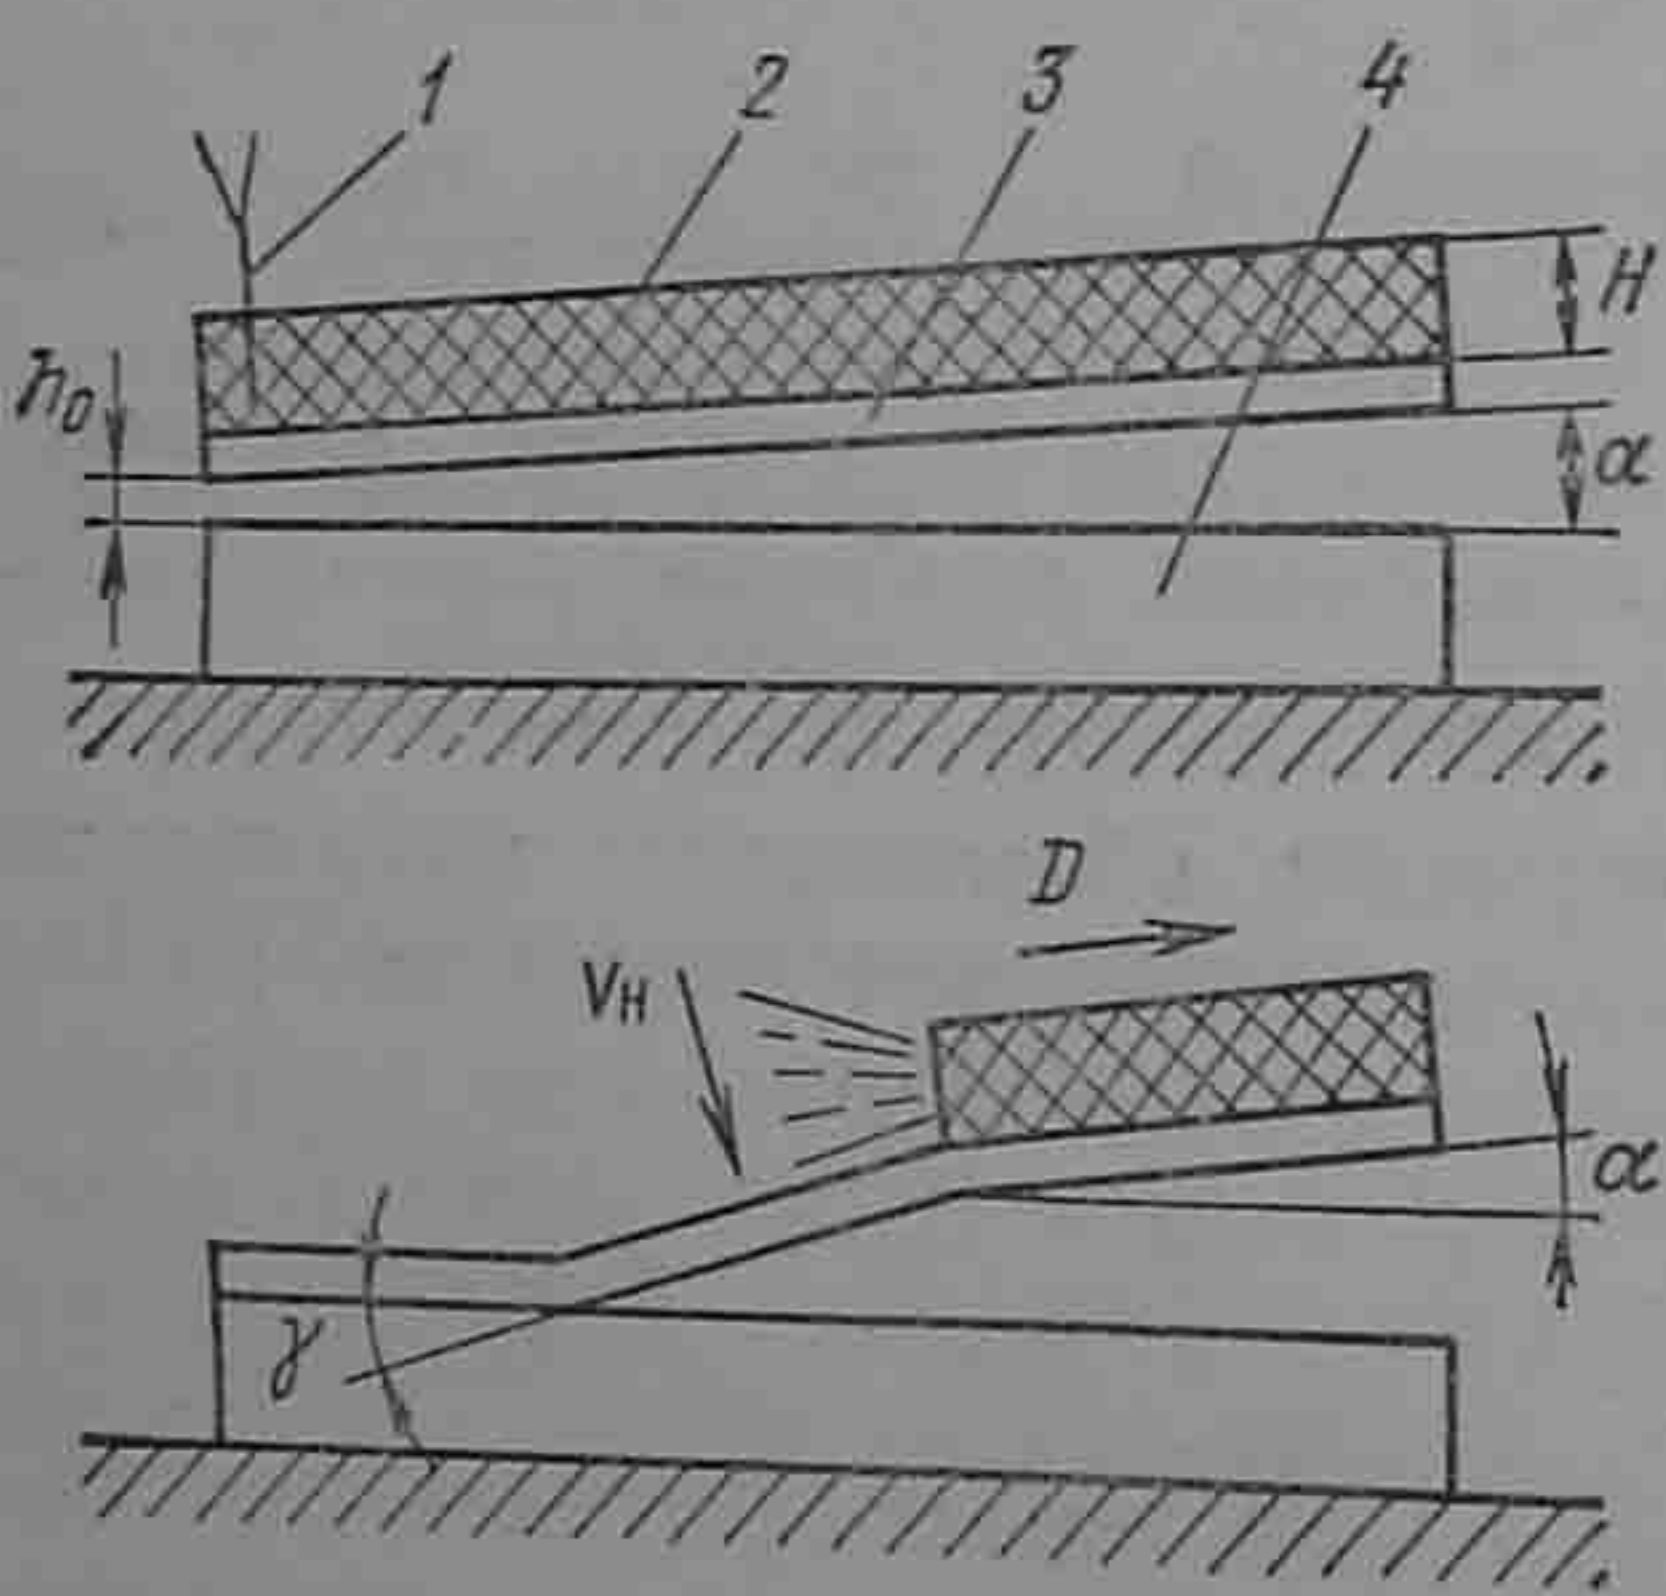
Принципиальная схема сварки взрывом
